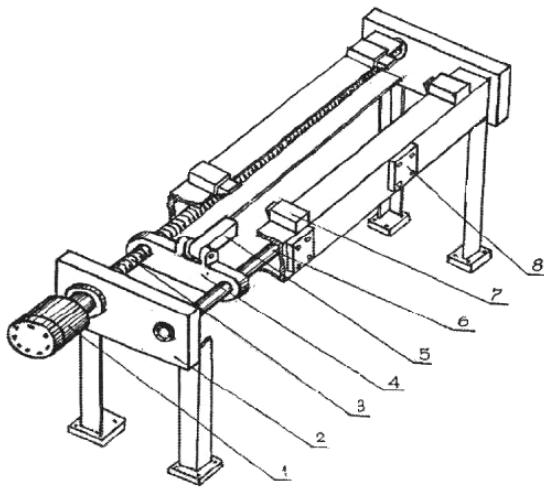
Схема загального виду механізму подачі заготовки: 1 – кроковий двигун, 2 – рама, 3 – ходовий гвинт, 4 – гайка, 5 – упор, 6 – опорний вал, 7 – фіксатори, 8 – датчики
